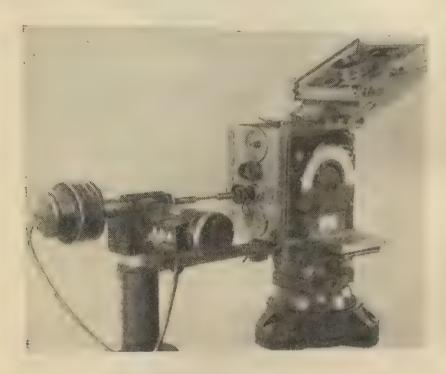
Приспособление для проверки фрикционных наматывателей киносъемочных аппаратов
